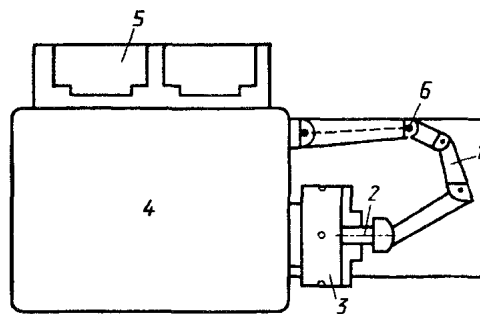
Шарнірний пристрій для підведення важкого патрона до шпинделя та відведення його до полиці: 1 - кронштейн; 2 - циліндрична цапфа; 3 - патрон; 4 — передня бабка токарного верстата; 5 - полиця; б - шарнір повороту та перевертання кронштейна
